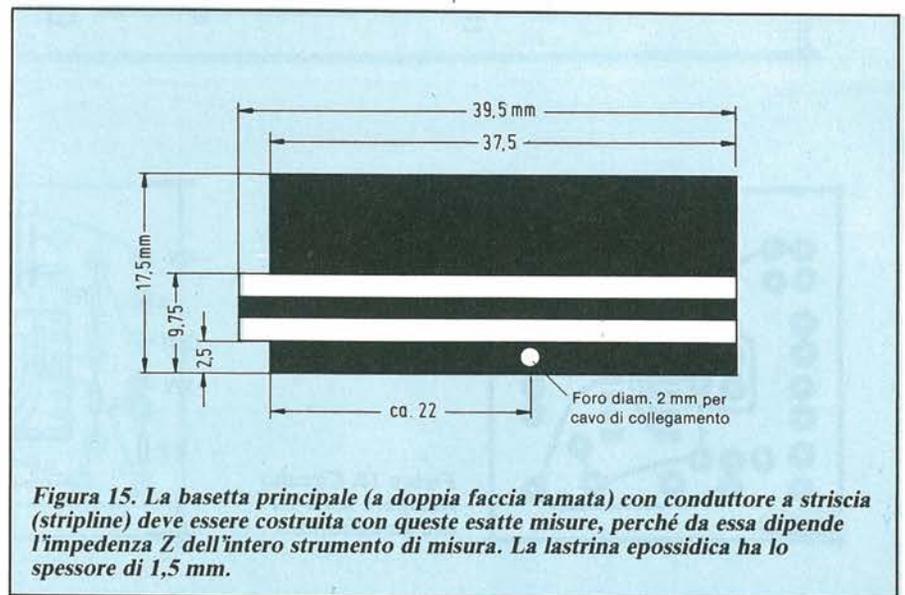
La basetta principale (a doppia faccia ramata) con conduttore a striscia (stripline) deve essere costruita con queste esatte misure, perché da essa dipende l'impedenza Z dell'intero strumento di misura. La lastrina epossidica ha lo spessore di 1,5 mm.
